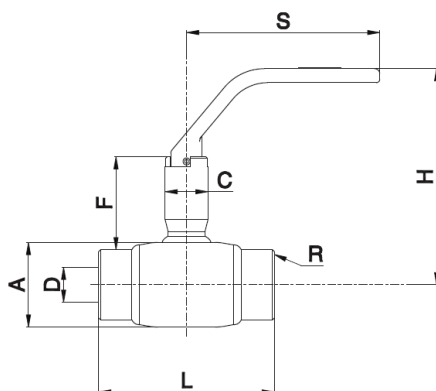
Габаритные и присоединительные размеры муфтовых шаровых кранов JiP-II.
